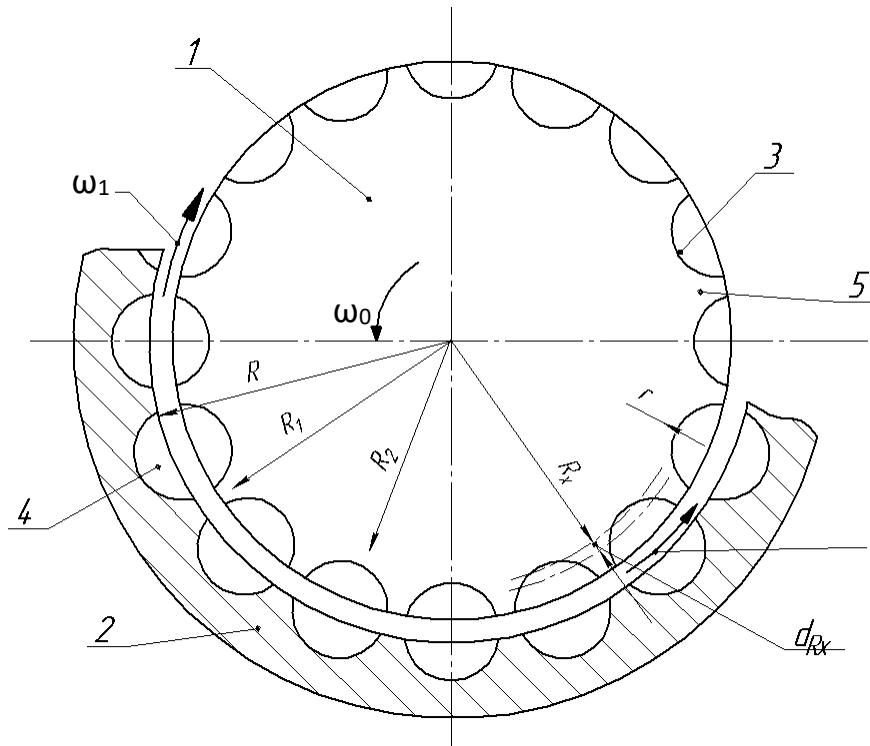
Схема визначення опорів лопатей ротора: 1 – ротор; 2 – статор; 3 - комірка ротора; 4 – комірки статора; 5 – лопатки ротора
